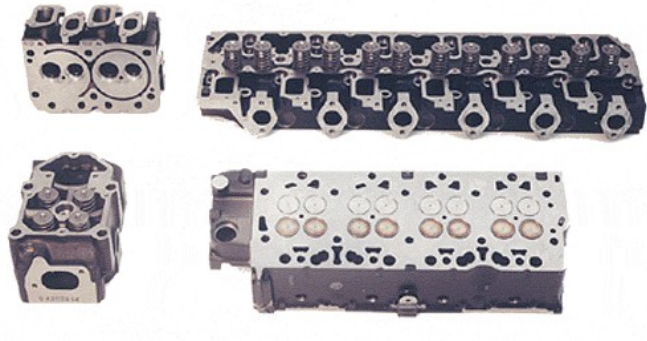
Imagen de una Culata de un Motor de Combustión Interna
